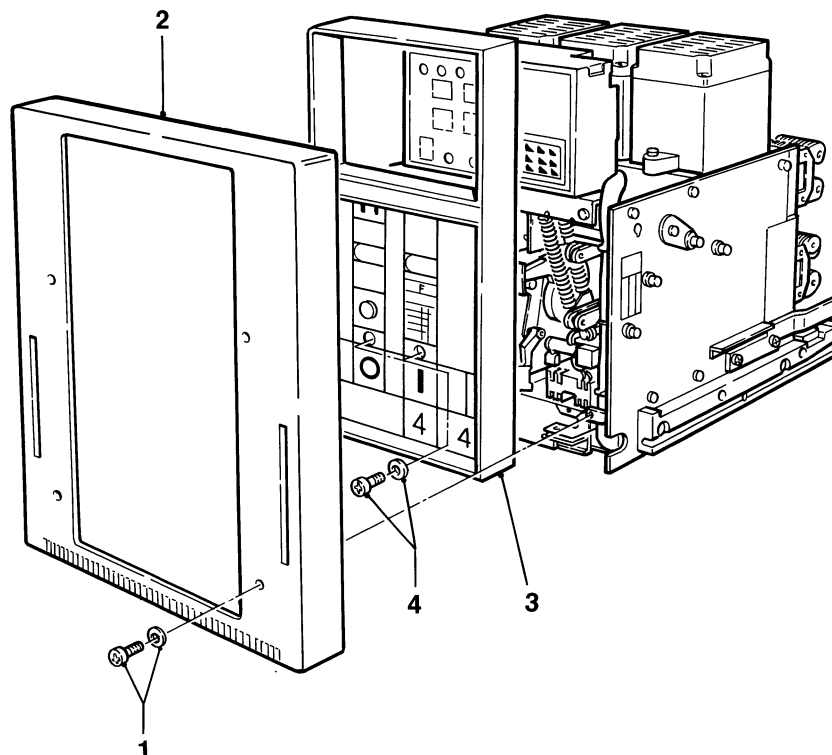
Rimozione della calotta del comando e dello scudo frontale dell'interruttore
